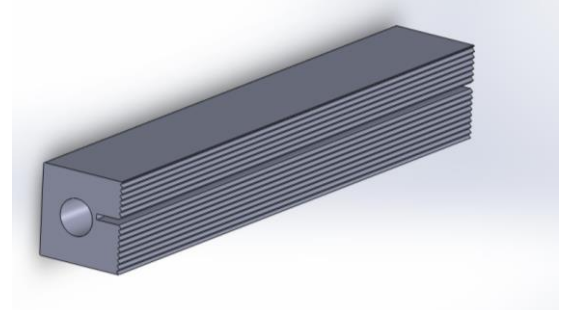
Pistón acoplado al mecanismo de corte
